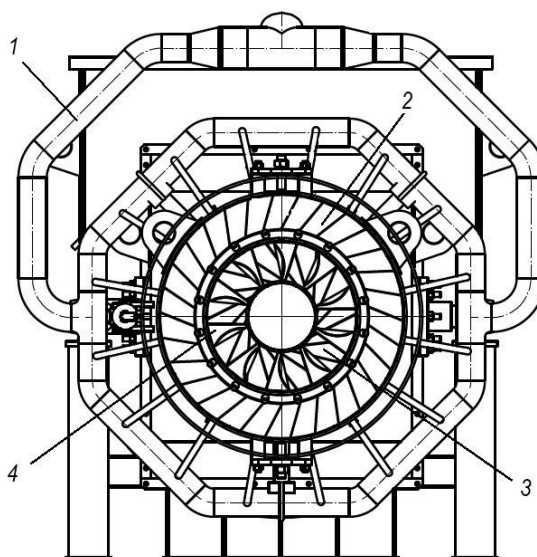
Вид горелки со стороны топki котла (1 – газовый коллектор; 2, 3 – аксиальный лопаточный аппараты каналов вторичного воздуха и аэросмеси; 4 – рассекатели потока аэросмеси)
